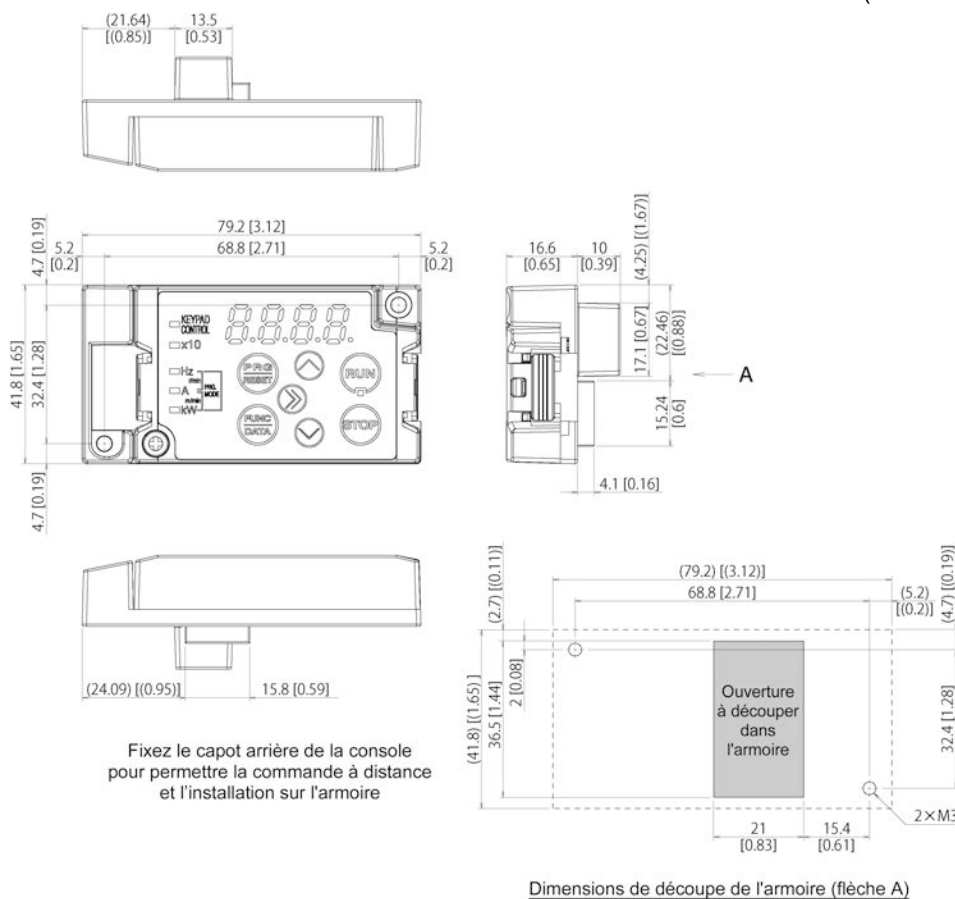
Emplacements des vis de fixation et dimensions de découpe de l'armoire
